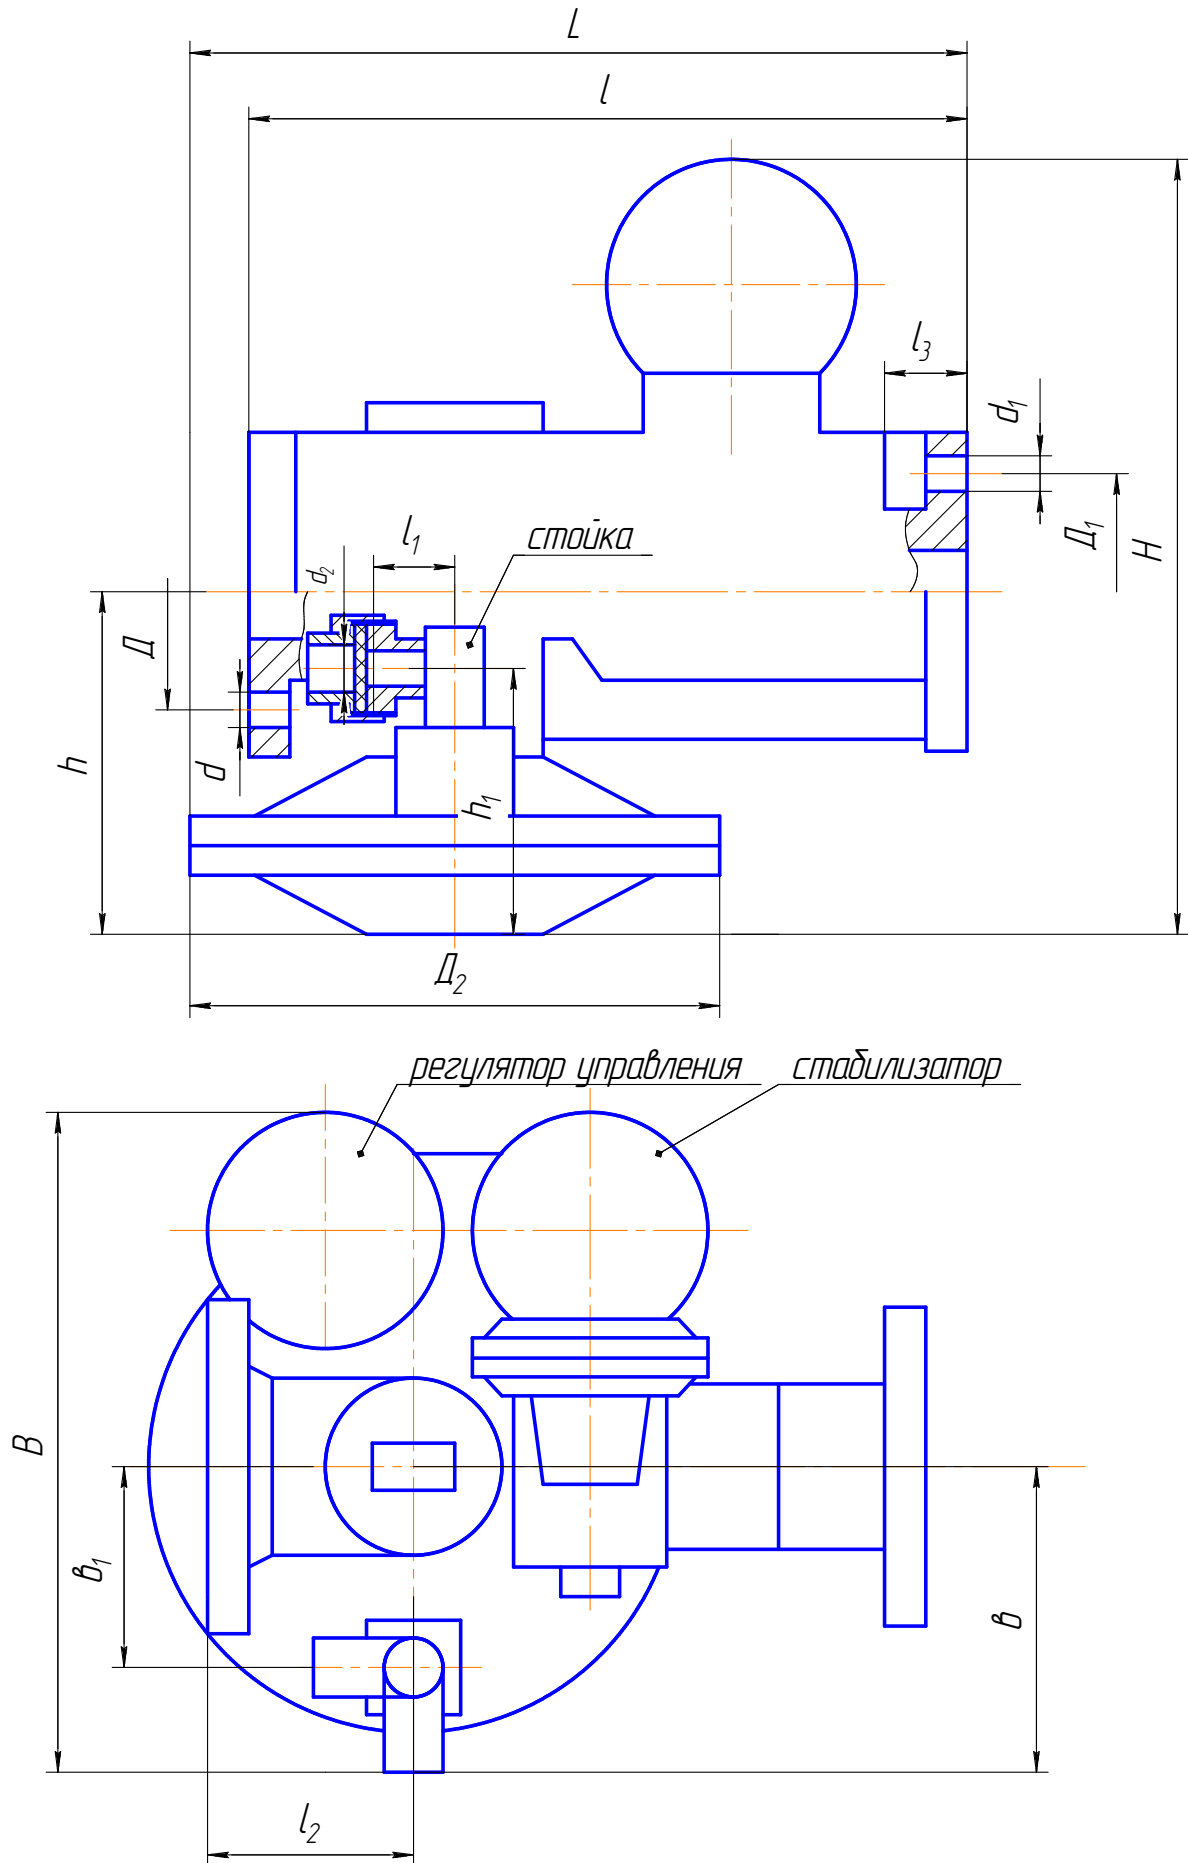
Габаритные и присоединительные размеры регуляторов
